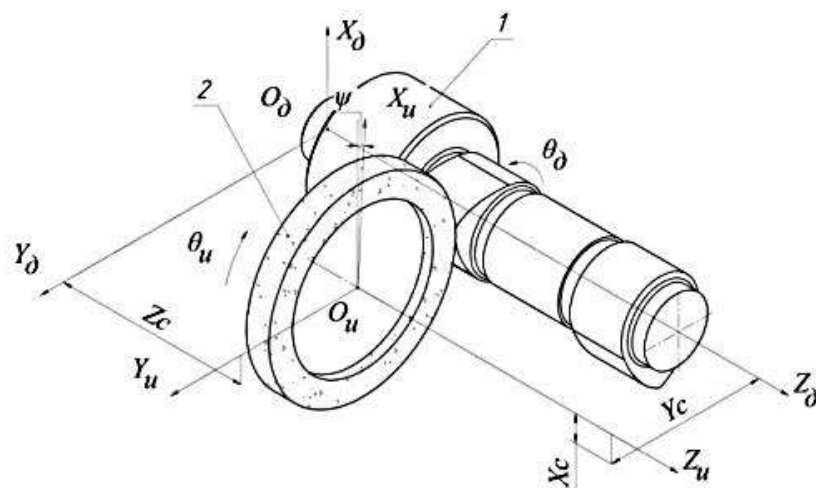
Розрахункова схема шліфування розподільного вала 1 Розподільний вал 2 абразивний круг
